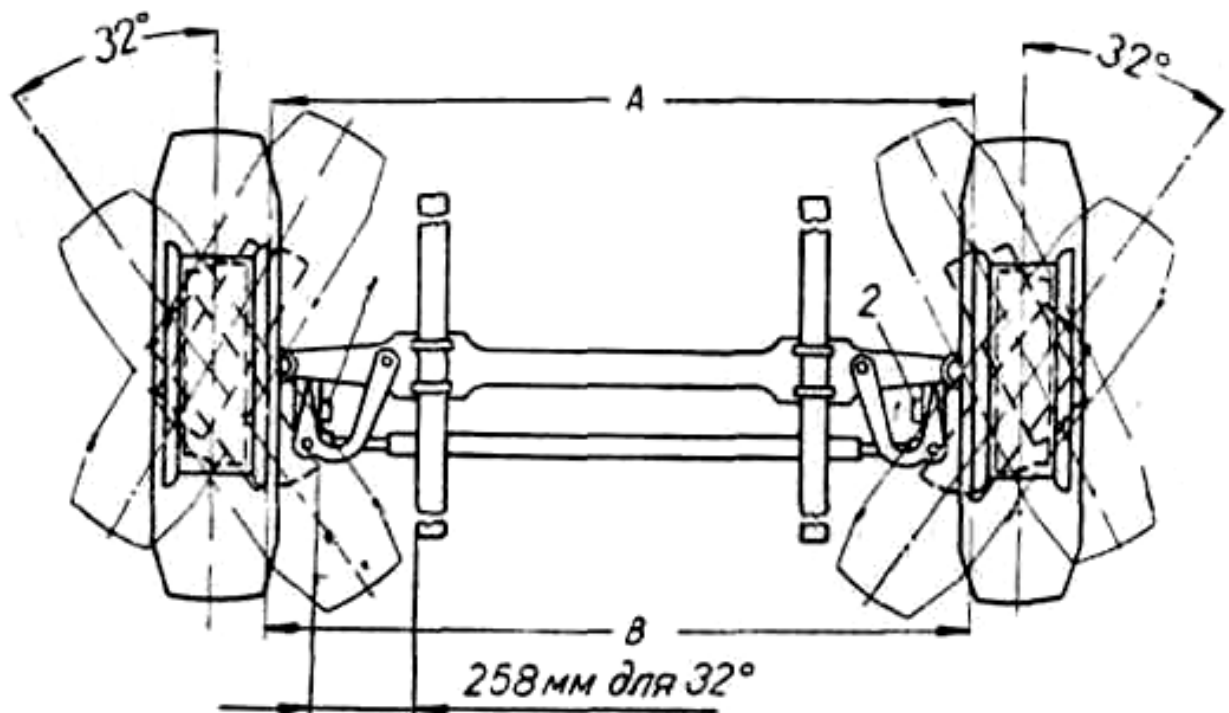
Установка коліс передньої підвіски: А – відстань між болтами коліс спереду; В – відстань між болтами коліс ззаду; 1 та 2 – упорні болти.
